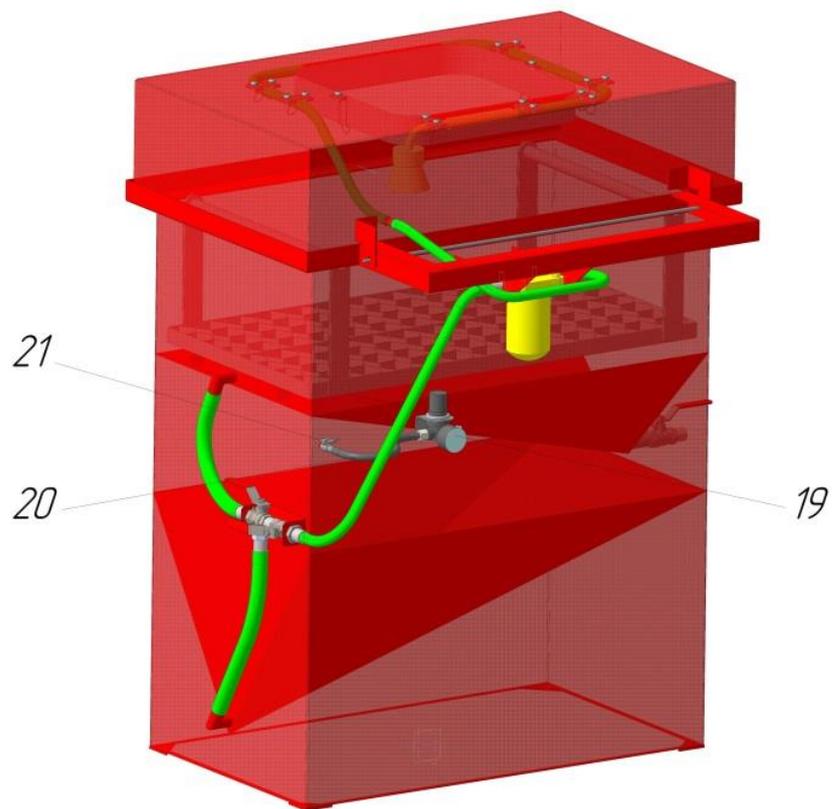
Вид установки сбоку (крышка закрыта)
